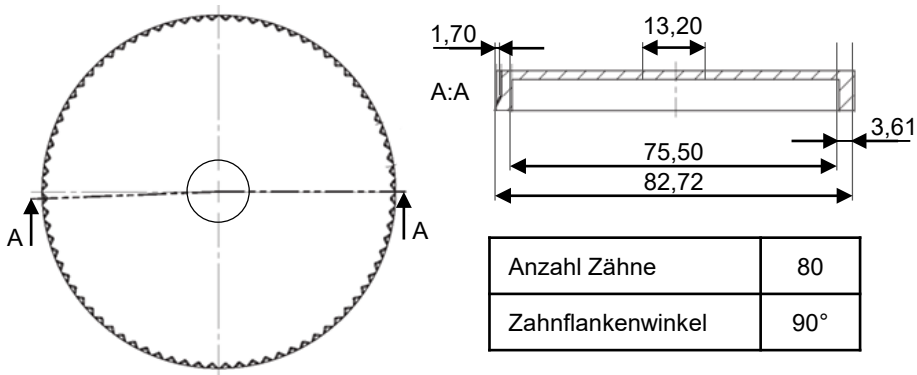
Demonstratorgeometrie des außenverzahnten Funktionsbauteils mit den durch die Werkzeuggeometrie vorgegebenen Abmessungen
